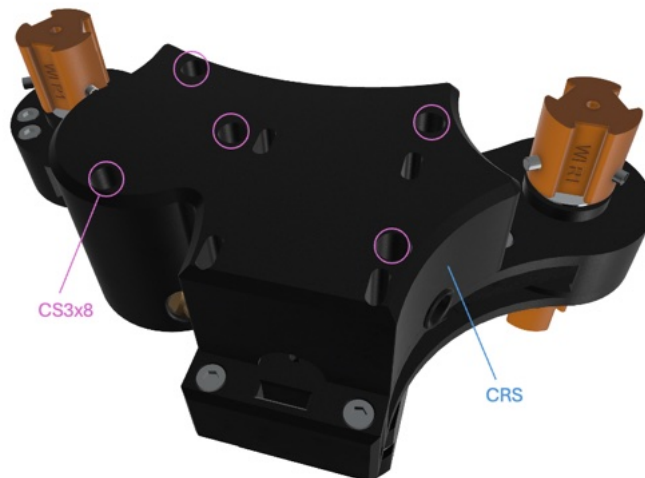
Rewinder-Chassis Montageschritt 27.
